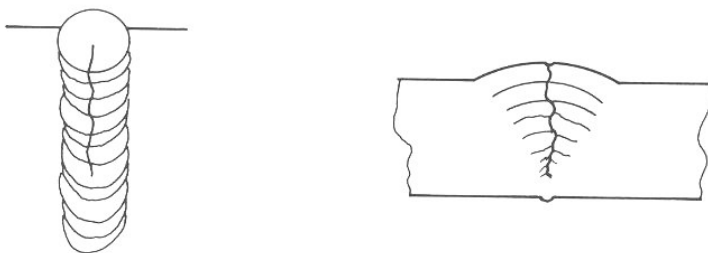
Fissuração no centro do cordão em um passe único de alta penetração
